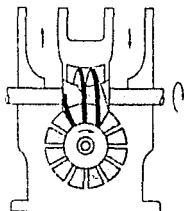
BOMBA DE DISCO Y TORNILLO
